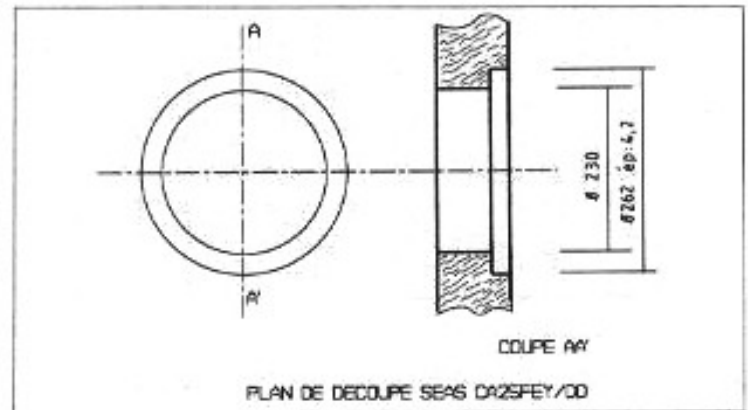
Plan de découpe de la façade avant pour le boomer SEAS CA25 FEY/DD.
